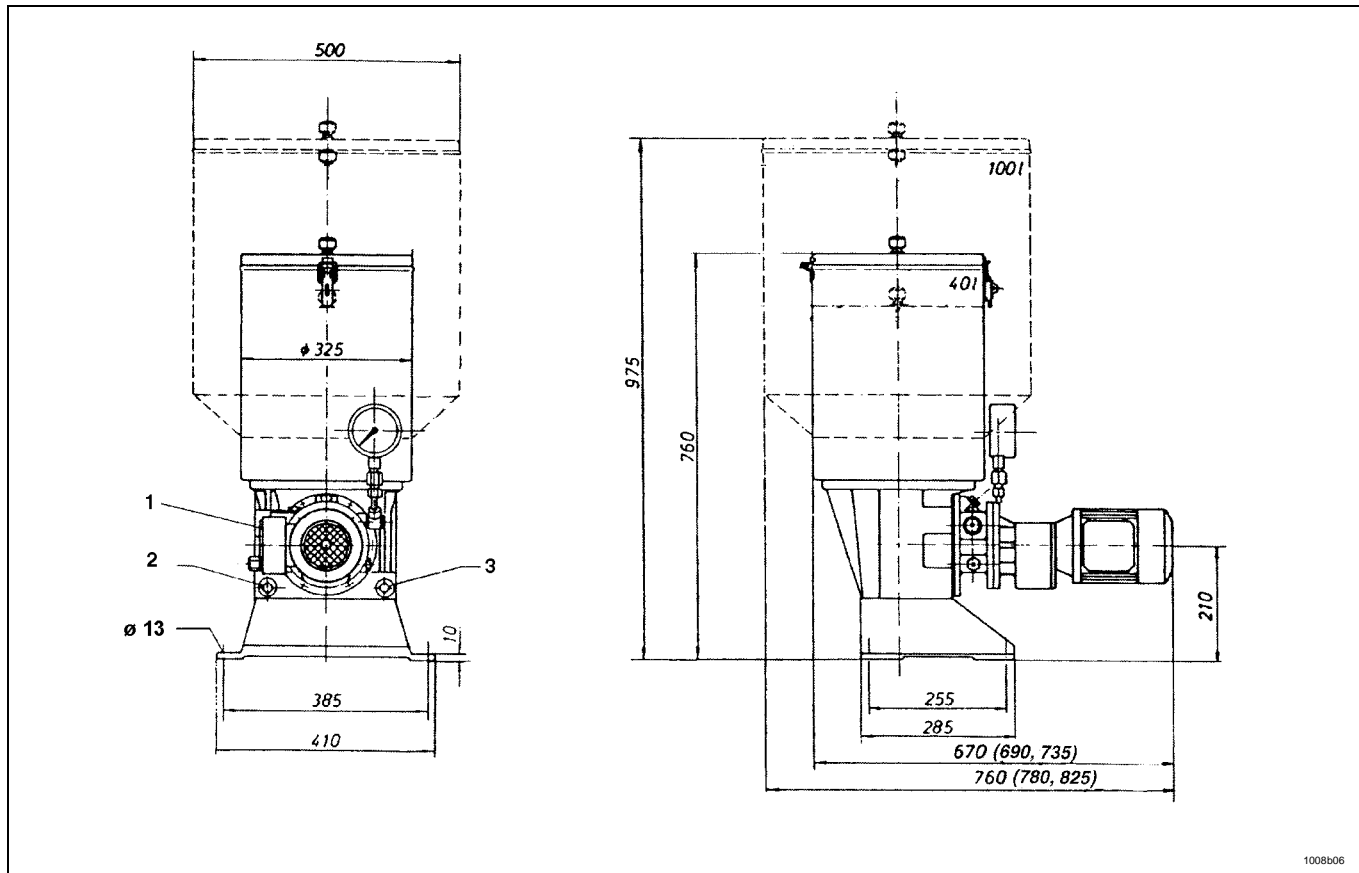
Abmessungen ZPU 08/14/24 mit Getriebeflanschmotor
